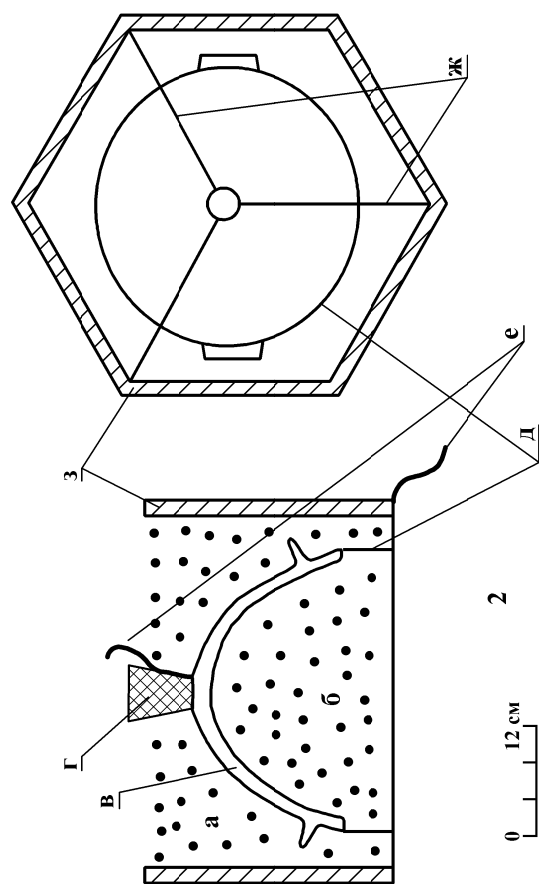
Формовка чугуновых котлов: а-верхняя полуформа; б-нижняя полуформа; в-модель котла; г-модель литника; д-вертикальный круговой разъем верхней и нижней полуформ; е-концы разделительного шнура; ж-вертикальные разъемы верхней полуформы; з-опока.
